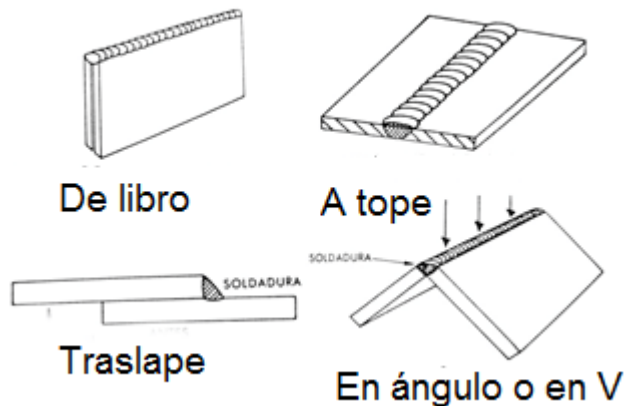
Diferentes tipos de unión a realizar con la soldadura de arco eléctrico.
